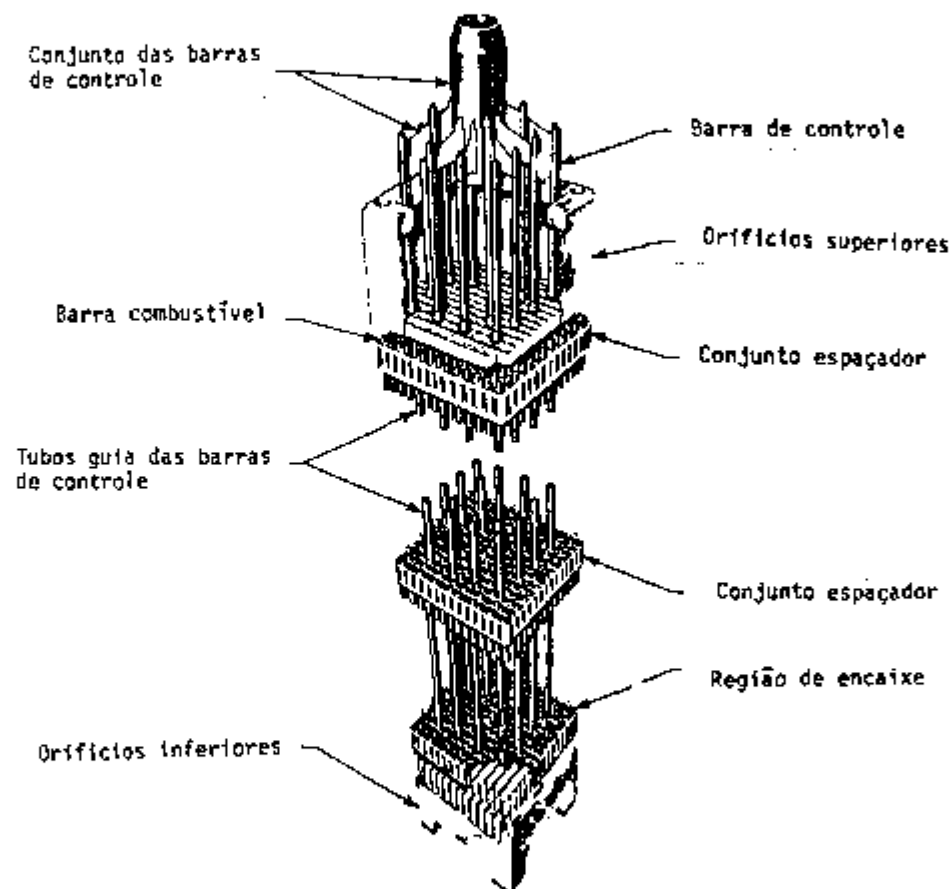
Esquema do conjunto combustível de um PWR /14/.
